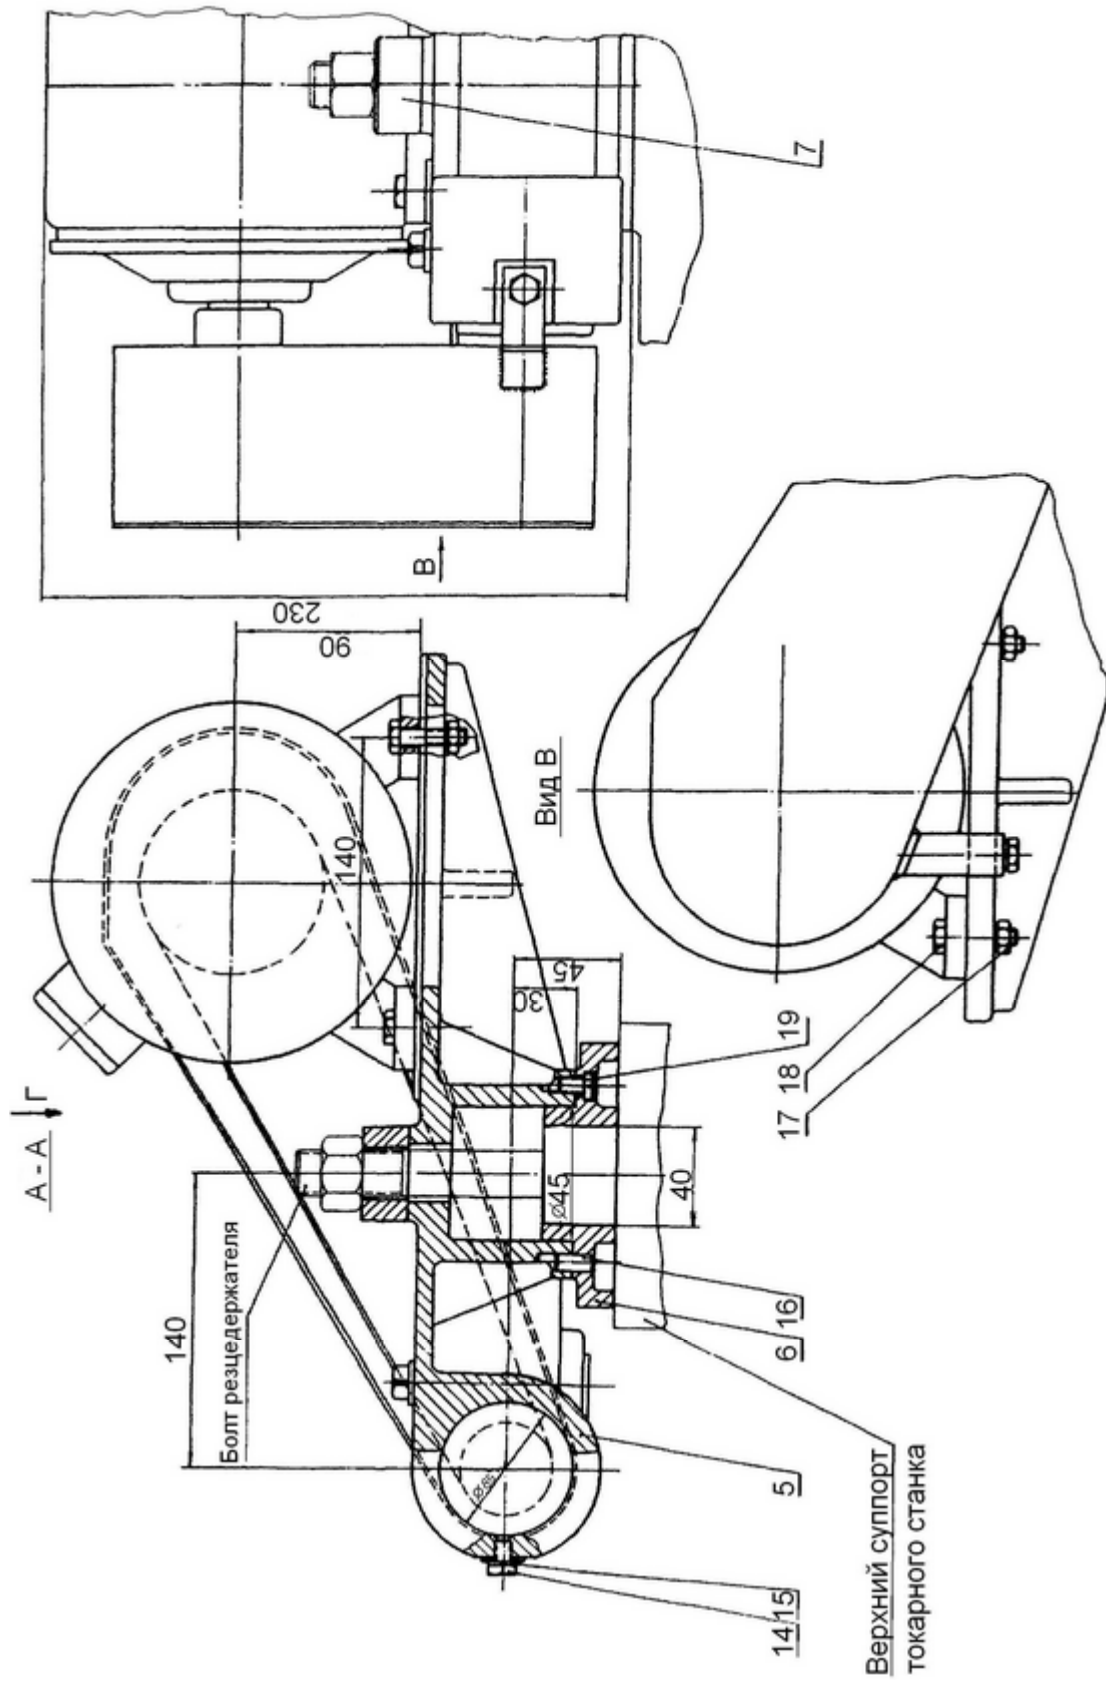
Приспособление для наружного, торцевого и внутреннего шлифования заготовок на токарных станках СД 7111 – 0001
